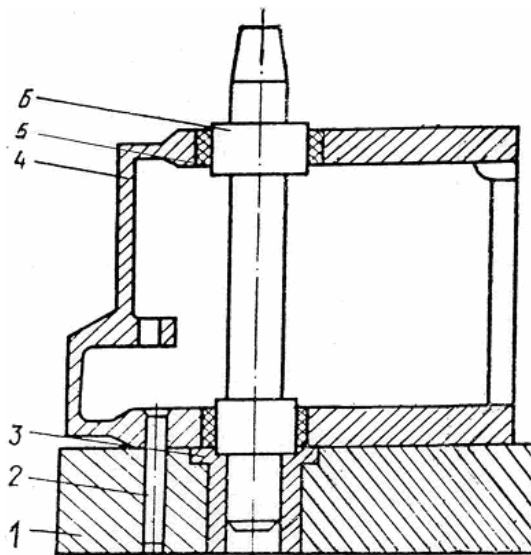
Схема формування посадочного місця під підшипник у гнізді корпусу компресора:
